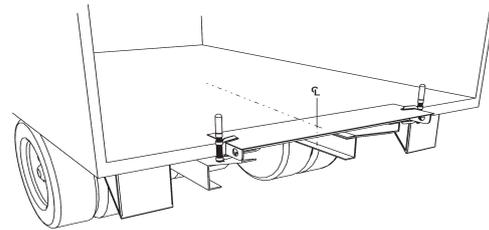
Montagevorrichtung mit Schraubzwingen, Schrauben oder per Punktschweißung an der Hecktraverse befestigen
